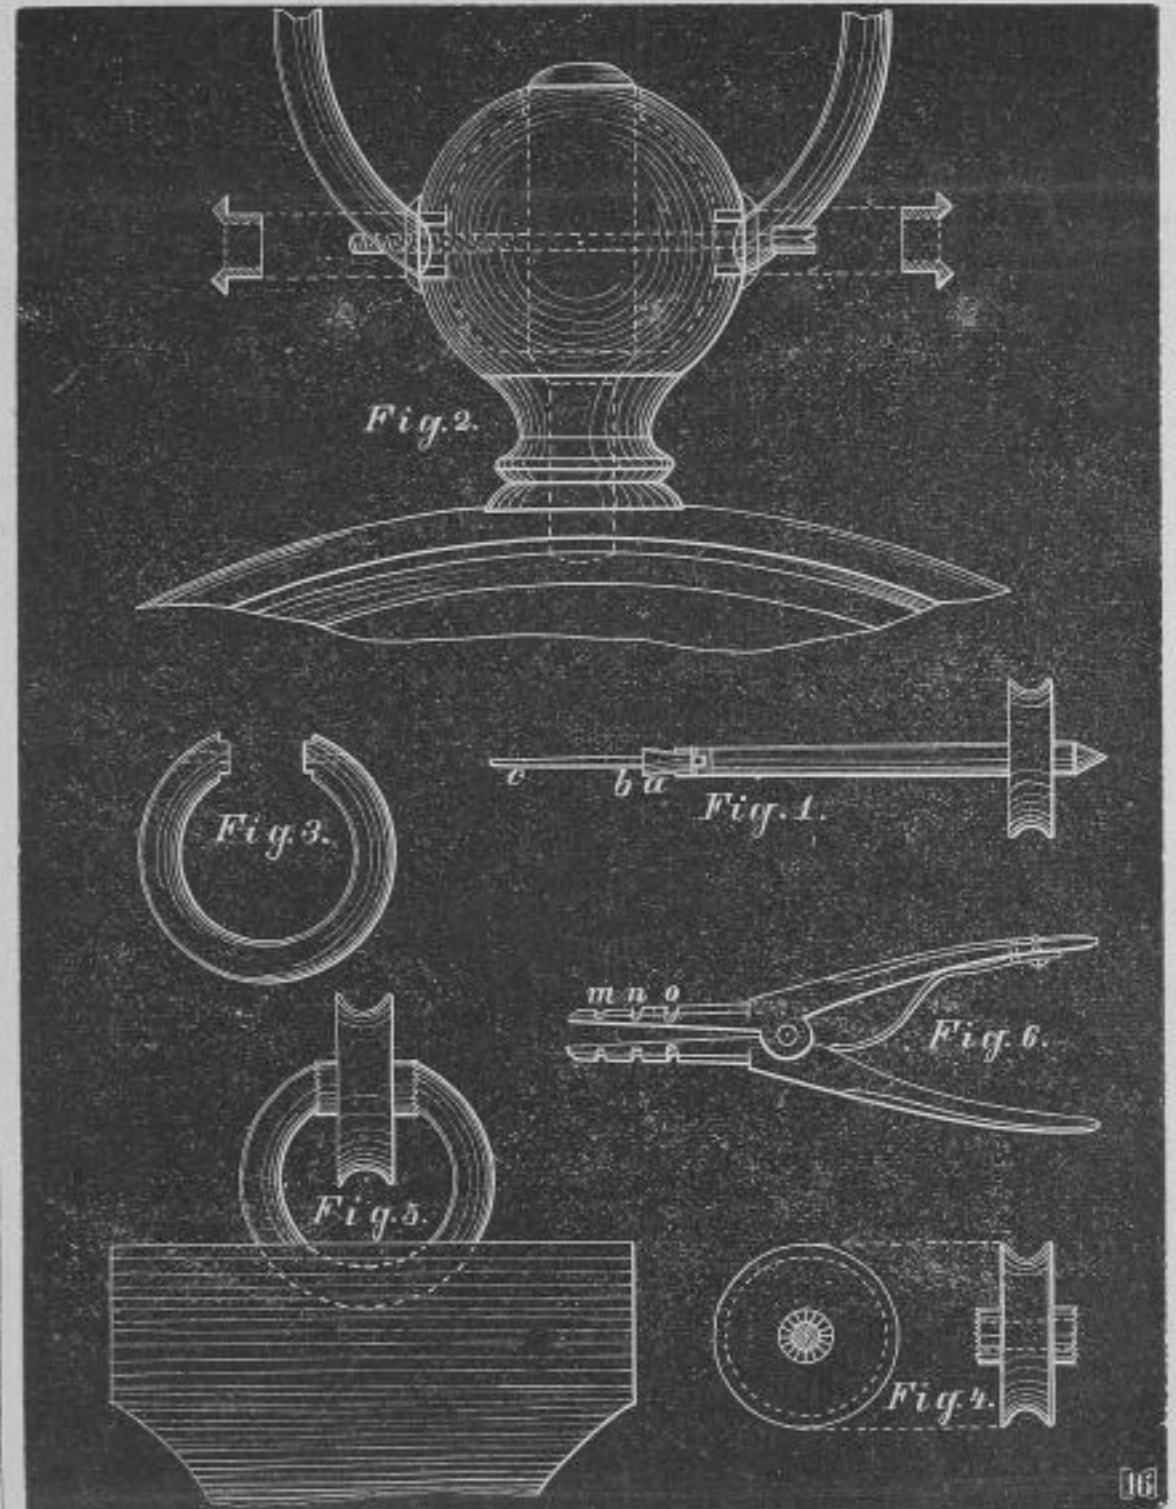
Fräse zur Einsenkung des Schraubenkopfes am Bügel. Fig. 4. Fräse für Bügelansätze. Fig. 6. Bügelzange.
